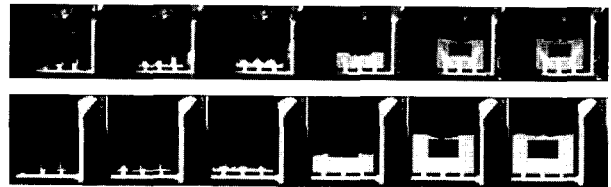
Mold Filling 과정의 실험 및 해석 결과(상-실험, 하-해석결과)(<http://www.castech.fi>)
